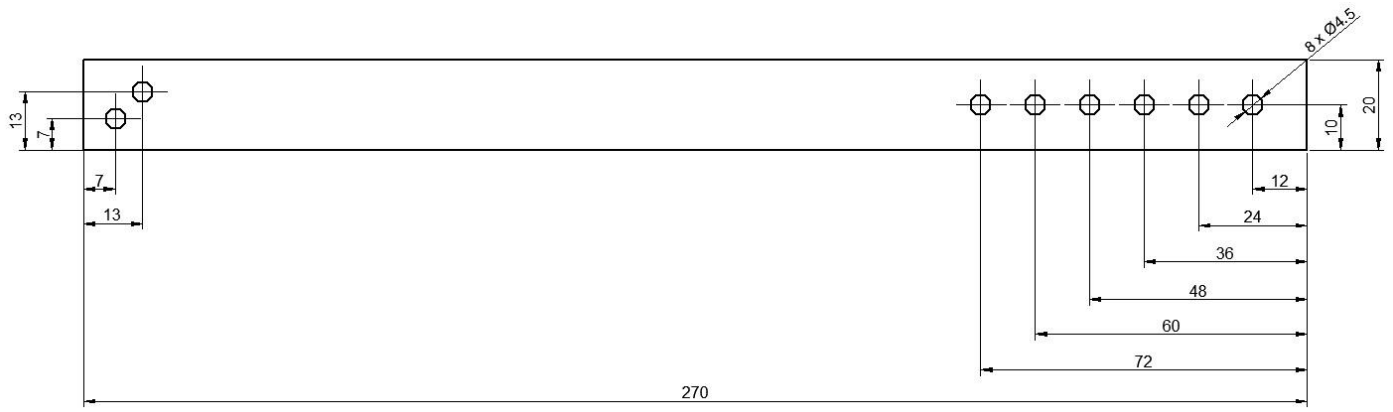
Widok bocznej i wierzchniej strony konstrukcji szkieletowej ramki tylnej
